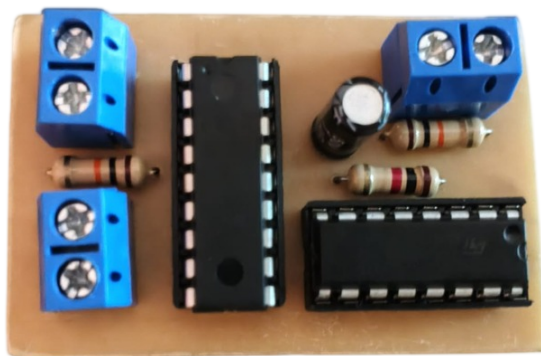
Montaje de los componentes en la placa PCB. Autor propio.
